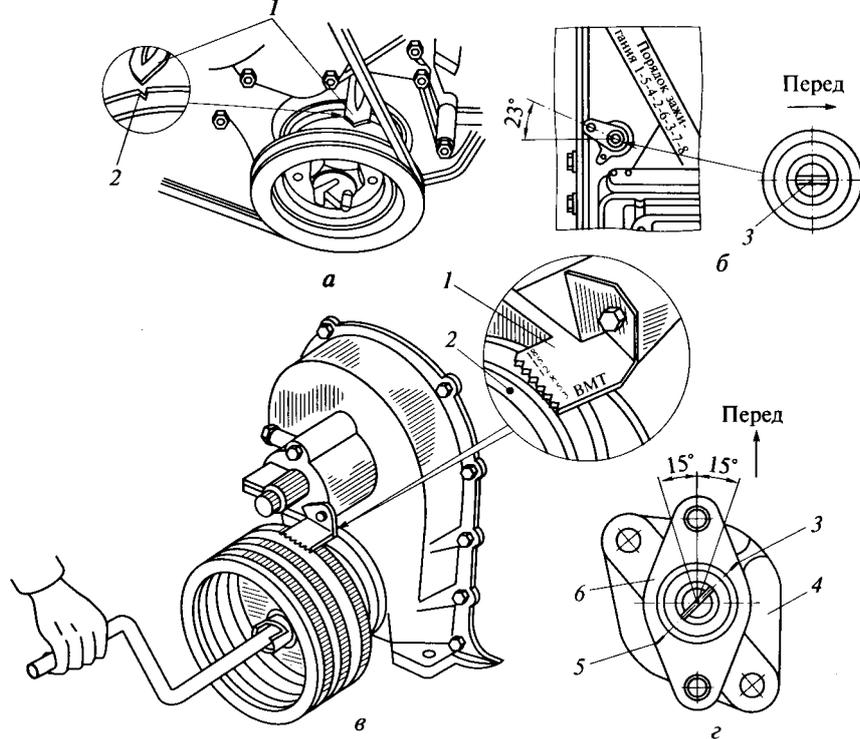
Метки для регулировки клапанов и установки зажигания:
